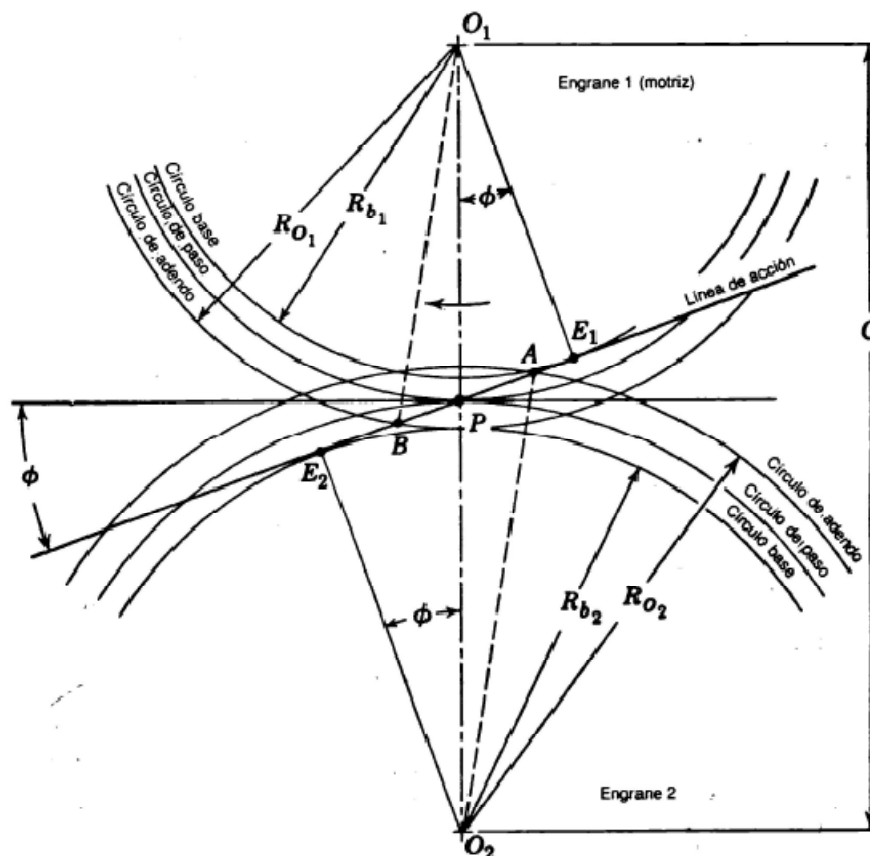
Ángulos de presión e involuta de dos engranajes acoplados
